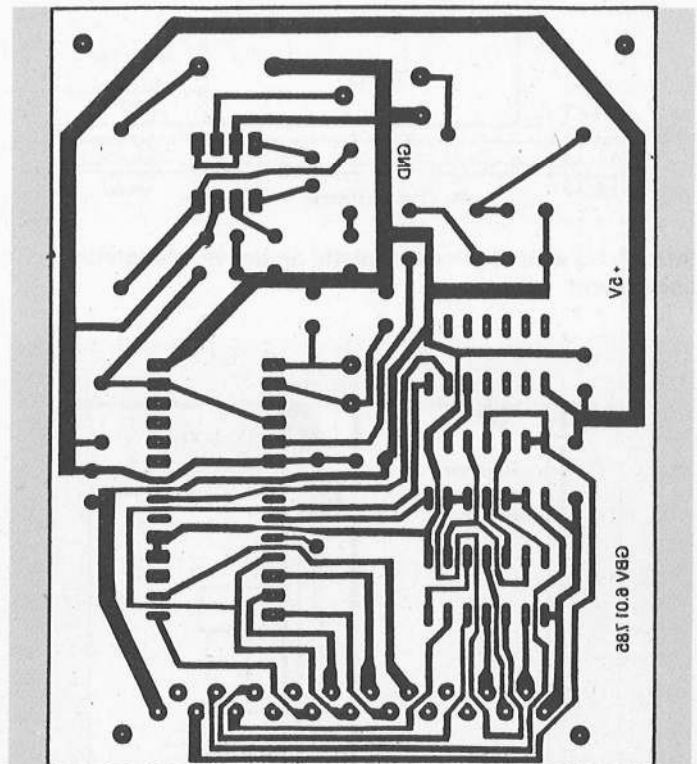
Das Platinenlayout für die Sprachausgabe-Karte (spiegelverkehrt)
